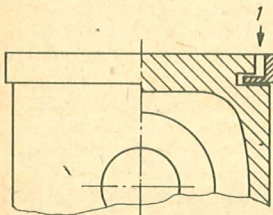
L-Kolbenring; er erhält seine Anpreßkraft durch den Gasdruck (1) im Zylinder
